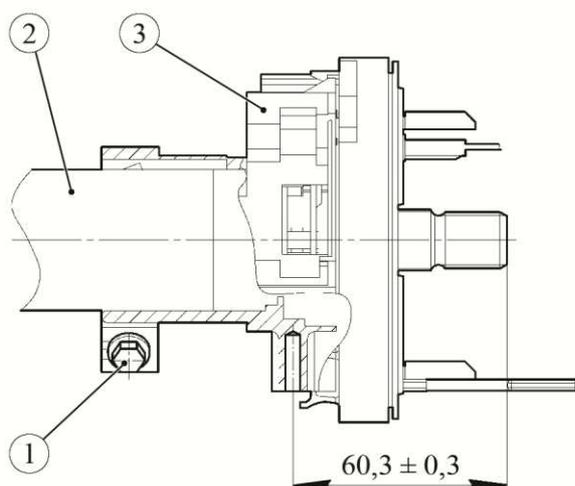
Установка соединителя с устройством вращающимся:
